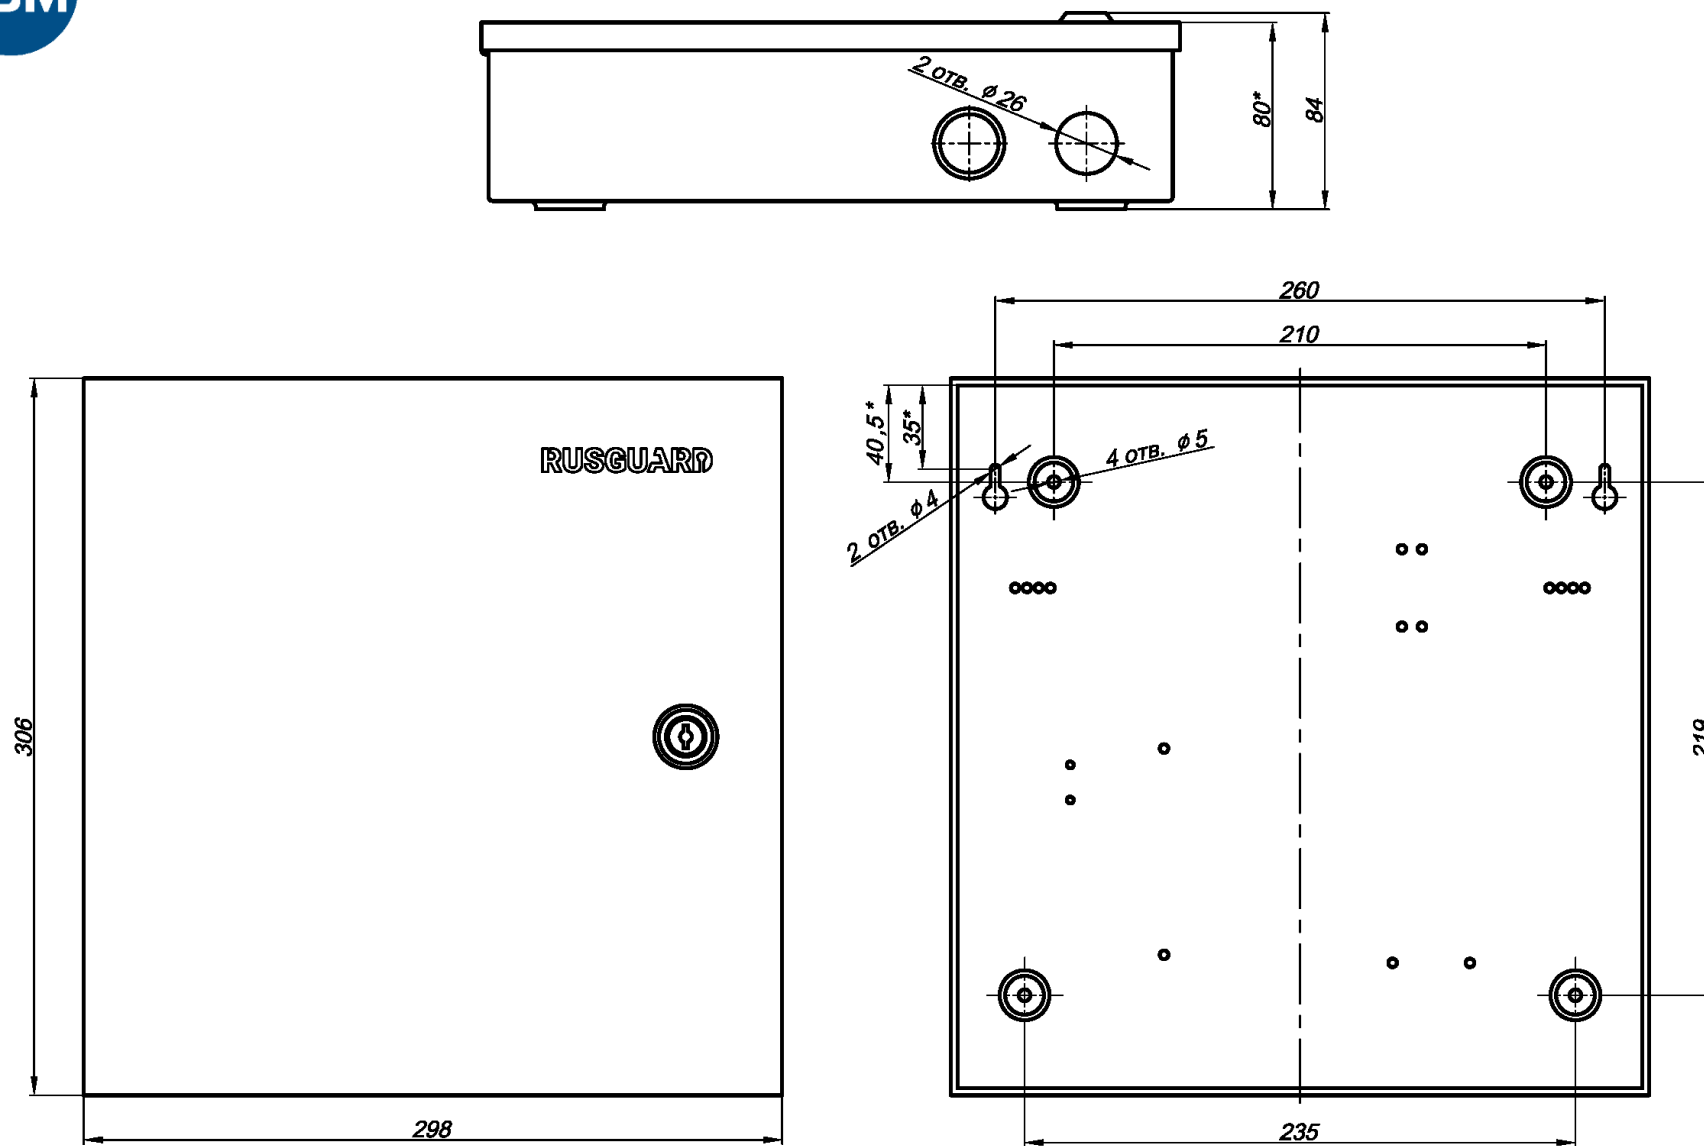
Габаритные размеры и крепеж контроллера в корпусе исполнения -BM
